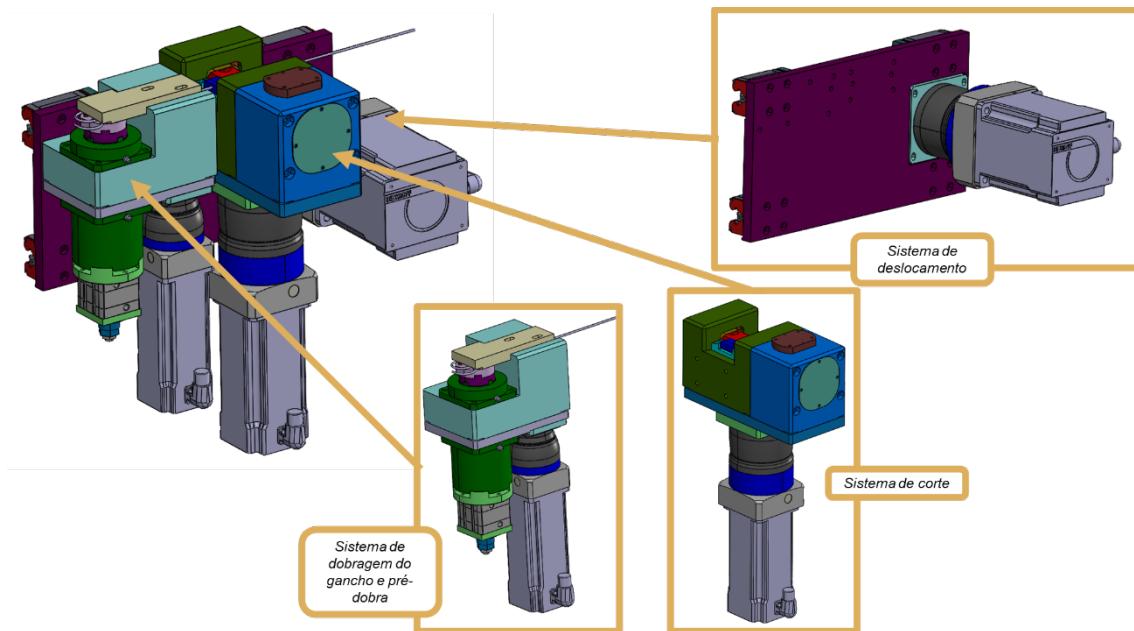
Dispositivo Gancho + Pré-dobra + Corte
